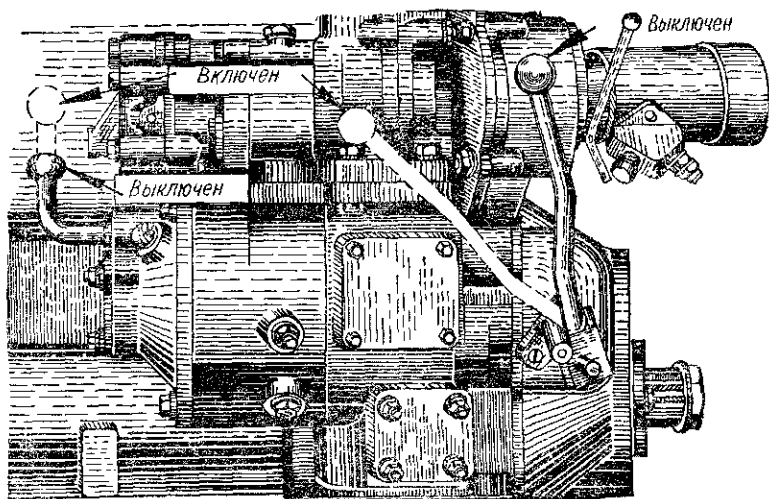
Положения рычага включения пусковой шестерни и рычага включения муфты редуктора пускового двигателя.
